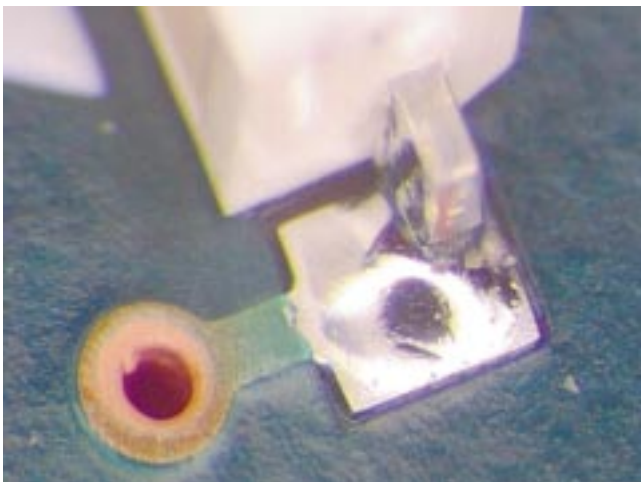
Soldadura SnPb; Acabado OSP
